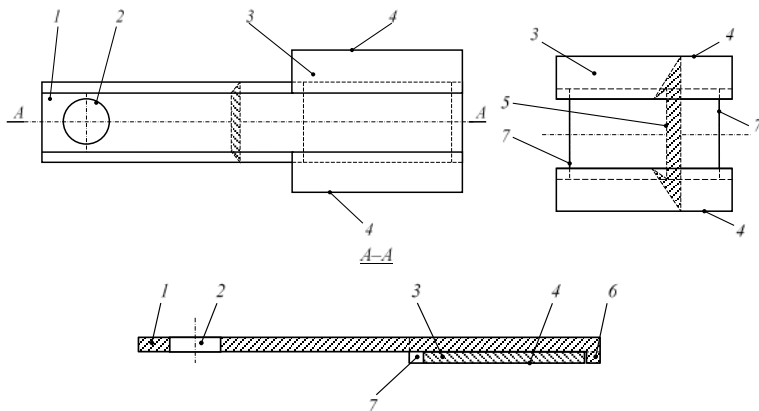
Нож роторной косилки с подвижной режущей накладкой: 1 – основание; 2 – отверстие для болта крепления; 3 – режущая накладка; 4 – режущие кромки; 5 – паз в накладке; 6 – выступ основания; 7 – вырез в накладке
